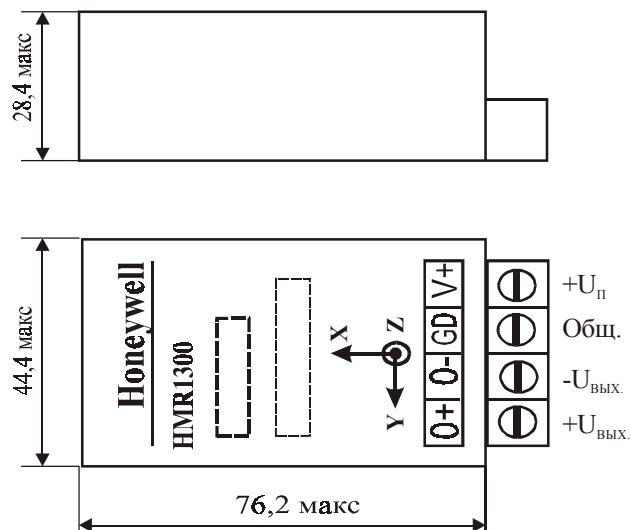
Внешний вид и габаритные размеры модуля типа HMR1300
